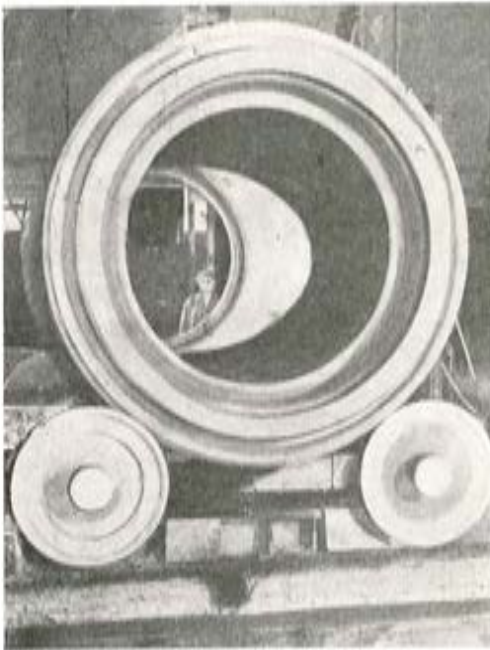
Hormigonado, por centrifugación, de una tubería de hormigón pretensado.
